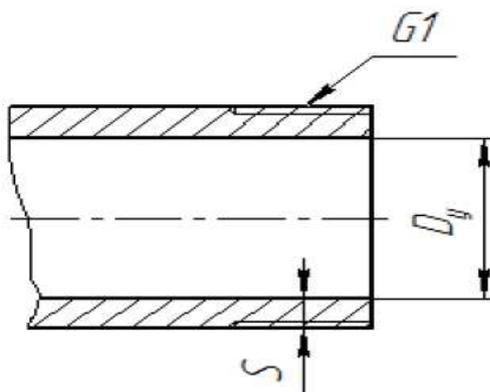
Обозначение трубной цилиндрической резьбы на чертеже
